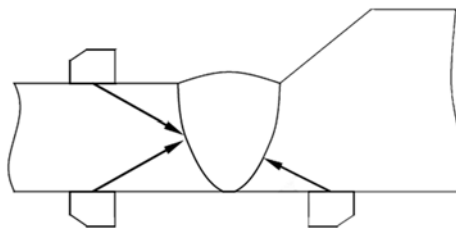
Схема контроля сварных соединений элементов, имеющих скосы кромок
